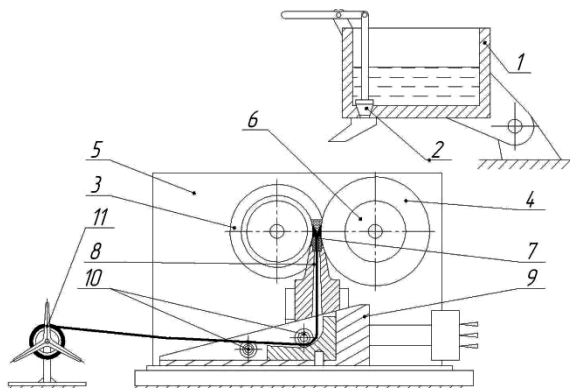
Устройство для непрерывного литья, прокатки и прессования:
